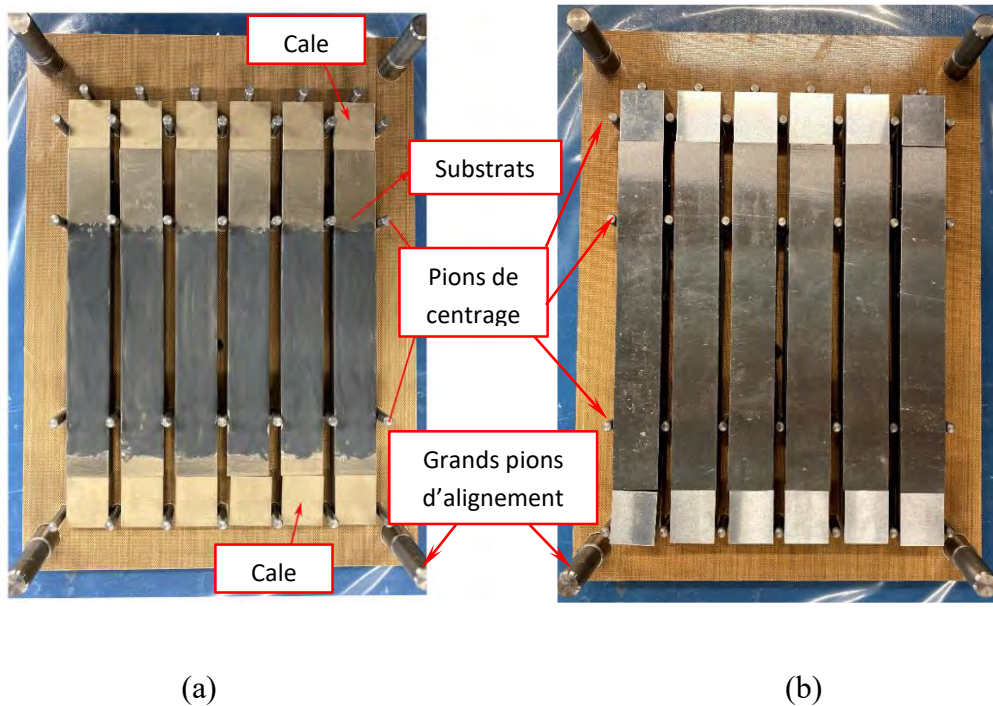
Positionnement des éprouvettes sur le moule : (a) substrat du bas avec l'adhésif, (b) éprouvette entière avant dépôt de la plaque supérieure.
